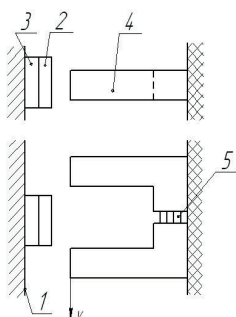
Конструкция датчика перемещения корпуса контейнера вибрационного станка: 1 – корпус контейнера; 2 – постоянный магнит; 3 – немагнитная прокладка; 4 – магнитопровод; 5 - модулятор
